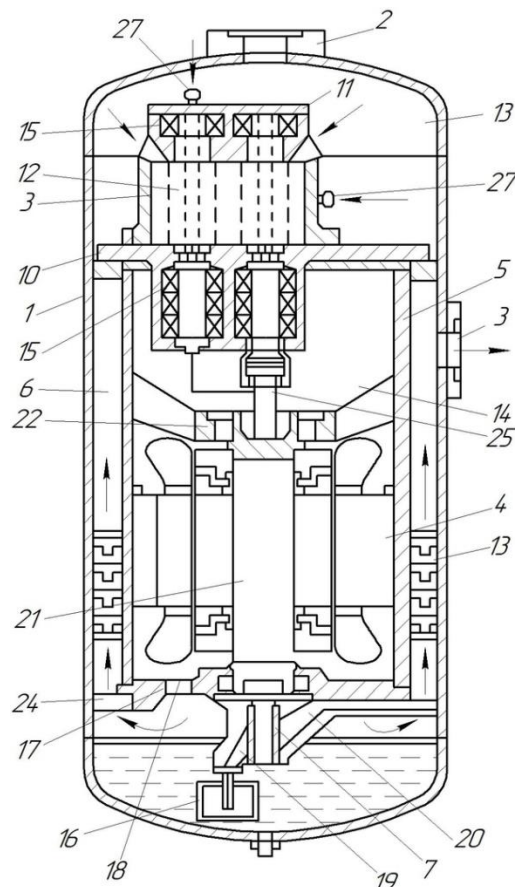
Герметичный вертикальный винтовой компрессор
